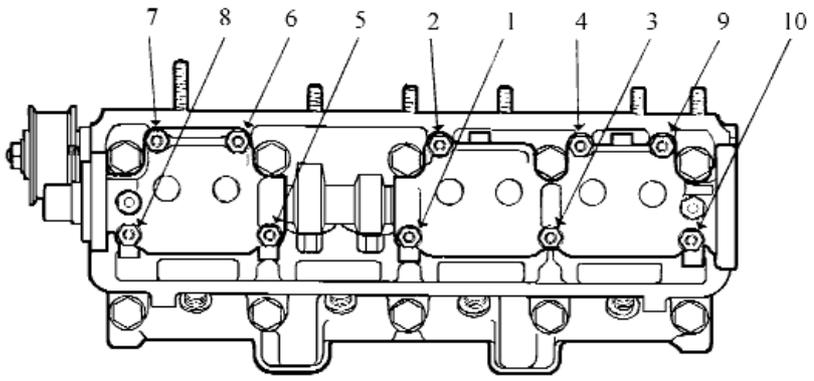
Порядок затягивания гаек крепления корпусов распределительного вала
